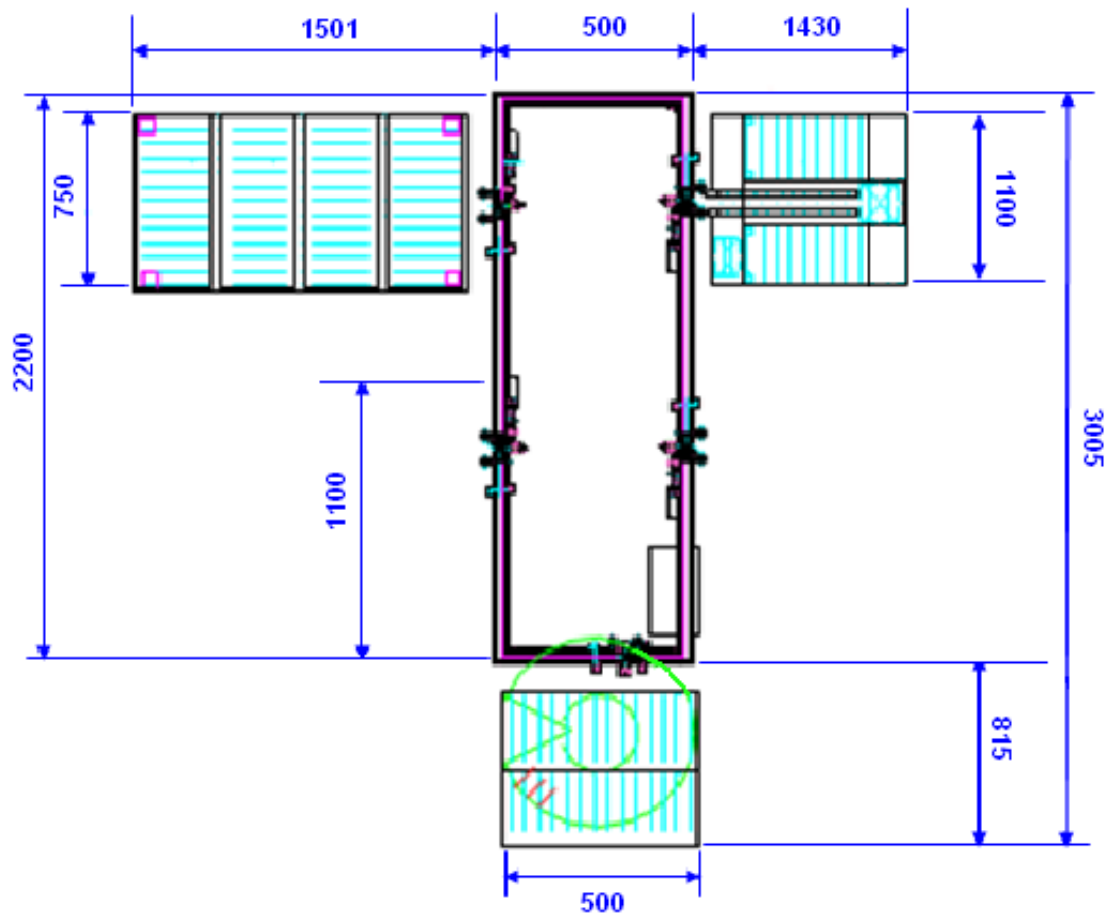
Plano de montaje y dimensionado del sistema FMS
